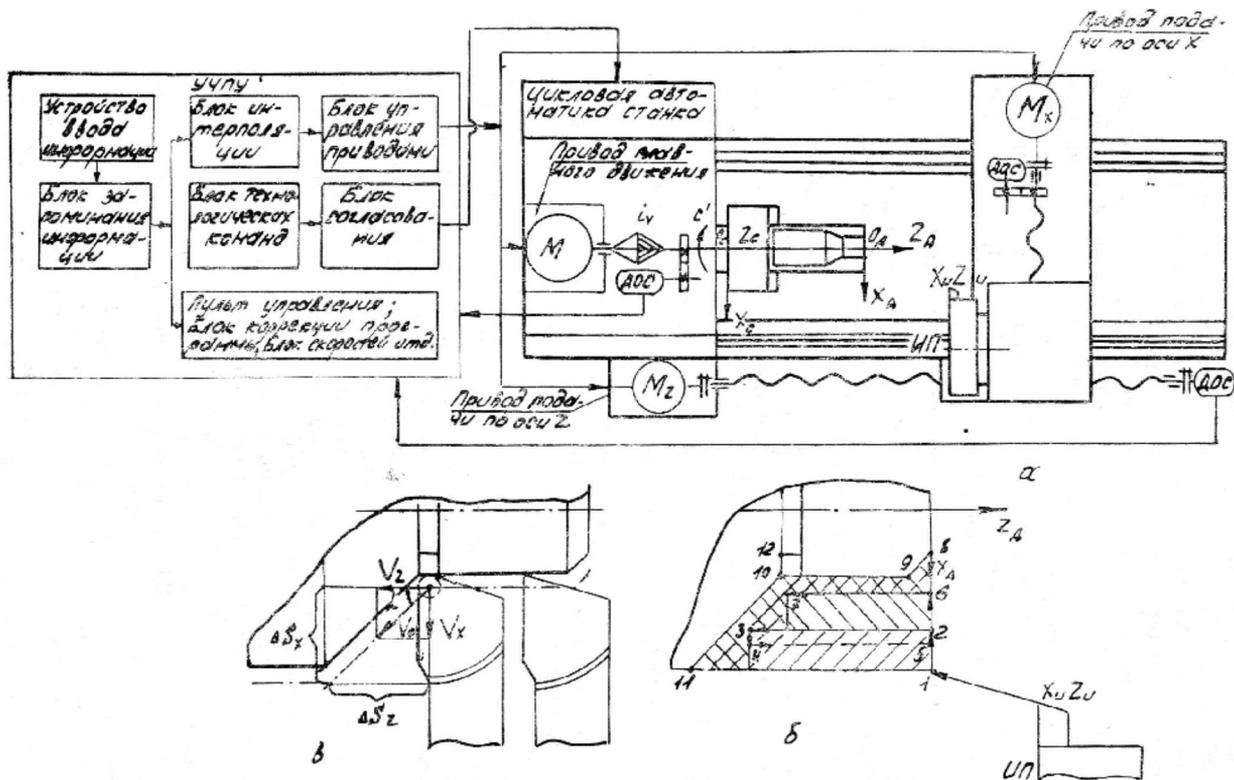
Токарний верстат з ЧПК: а – структура числового програмного керування токарним верстатом; б – схема переміщень інструменту під час виготовлення деталі; в – формування швидкості подачі вздовж контуру
